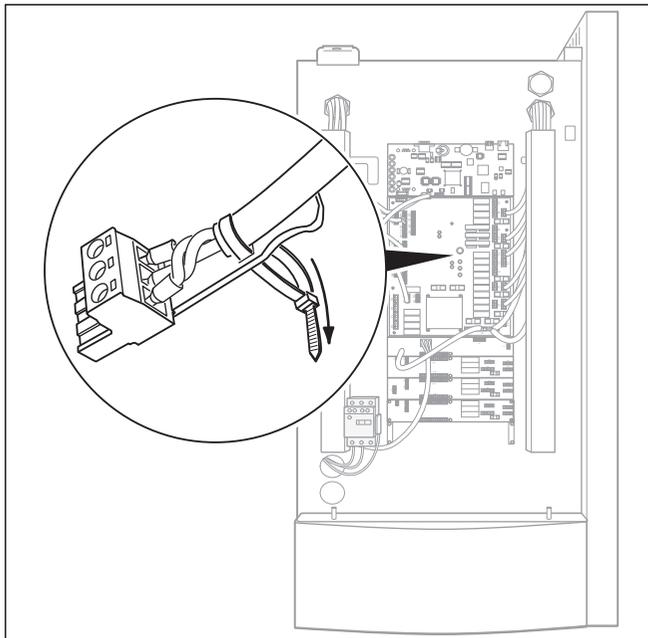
Kabel an Zugentlastung mit Kabelbinder befestigen
